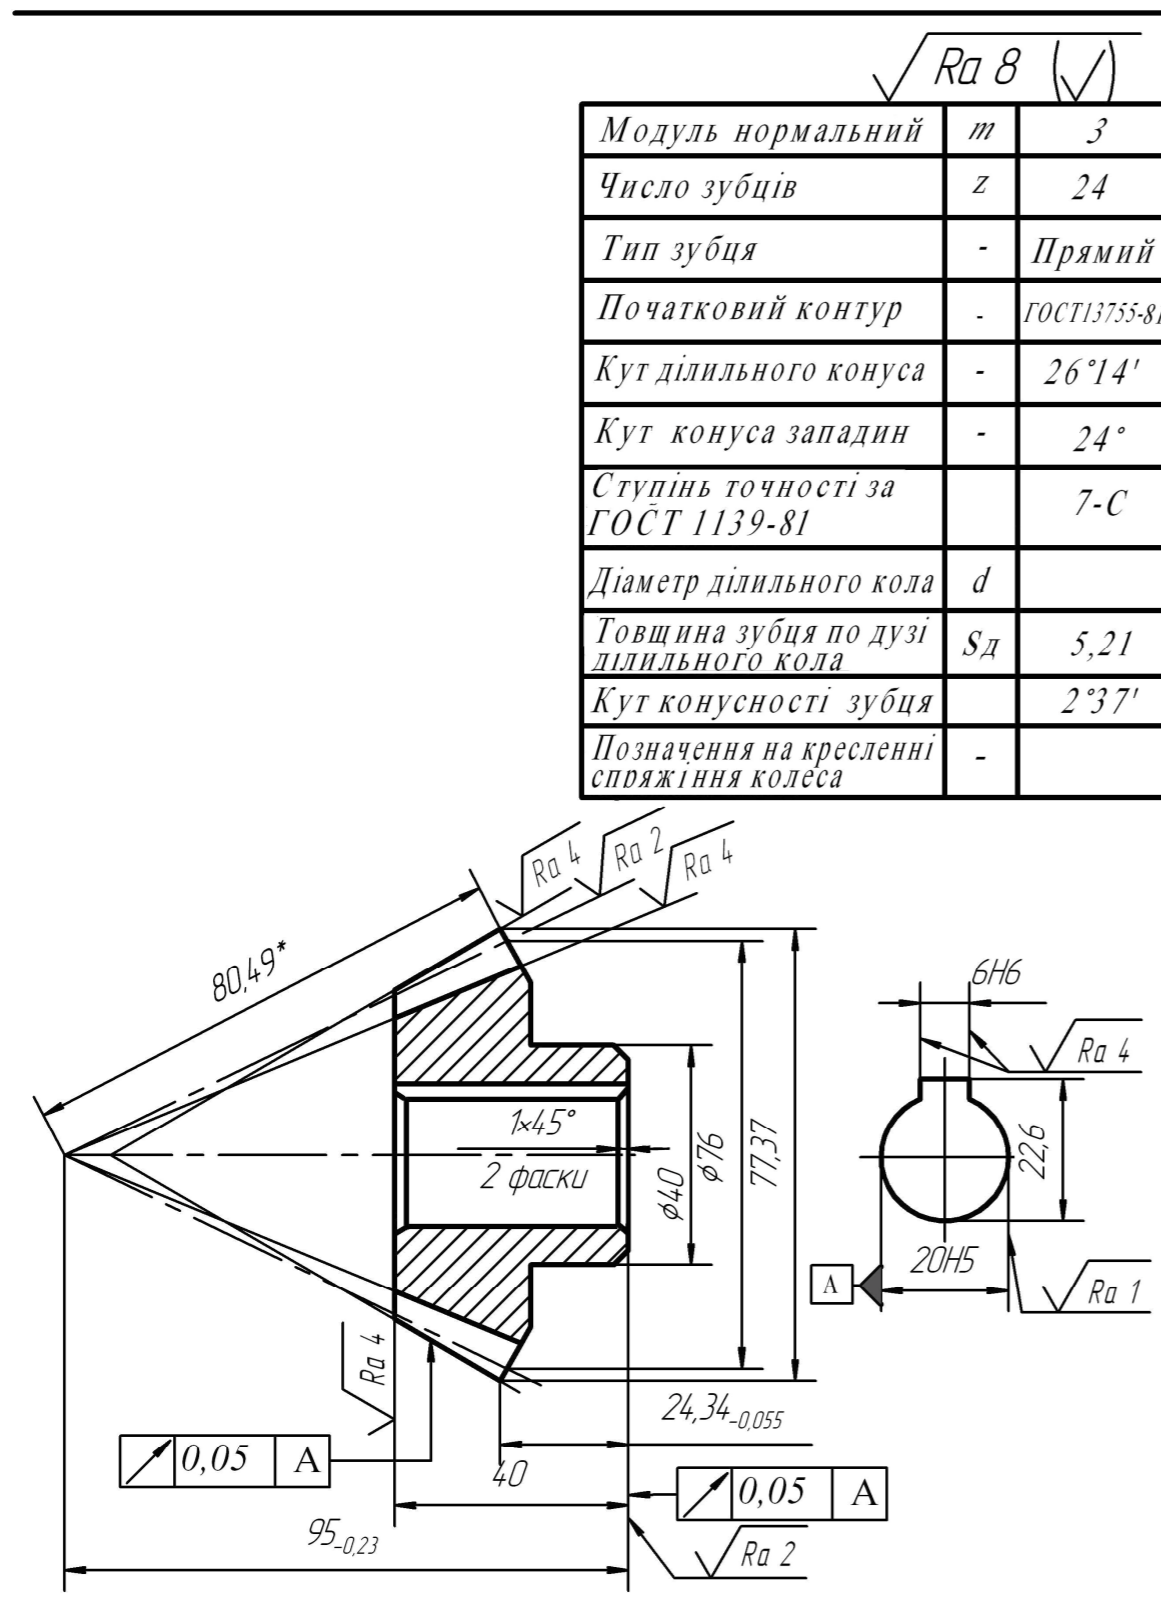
Приклад робочого креслення конічного зубчастого колеса з прямими зубцями
